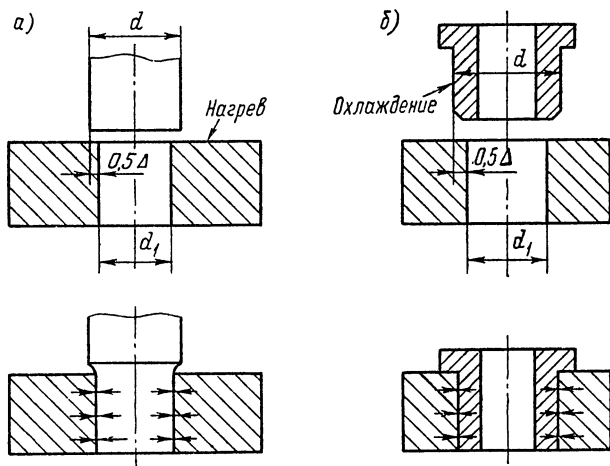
Схема соединений с нагревом (а) охватывающей или охлаждением (б) охватываемой детали
